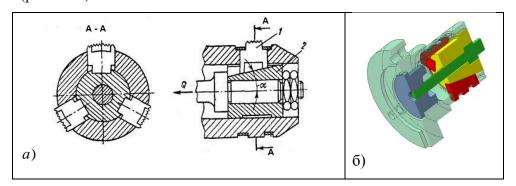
Клиноплунжерная оправка с трехскосым клином: а) сборочный чертеж оправки; б) 3-D модель аналогичной оправки;
